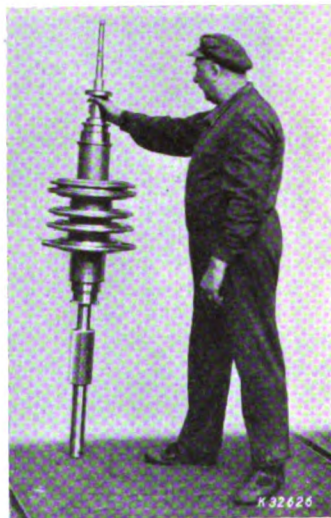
Läufer einer Getriebeturbine, 700 kW, 12 000 U/min.
